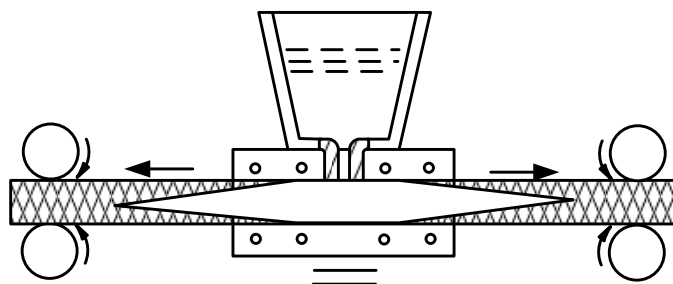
Схема МНЛЗ с двусторонним вытягиванием заготовки конструкции ВНИИМЕТМАШ
